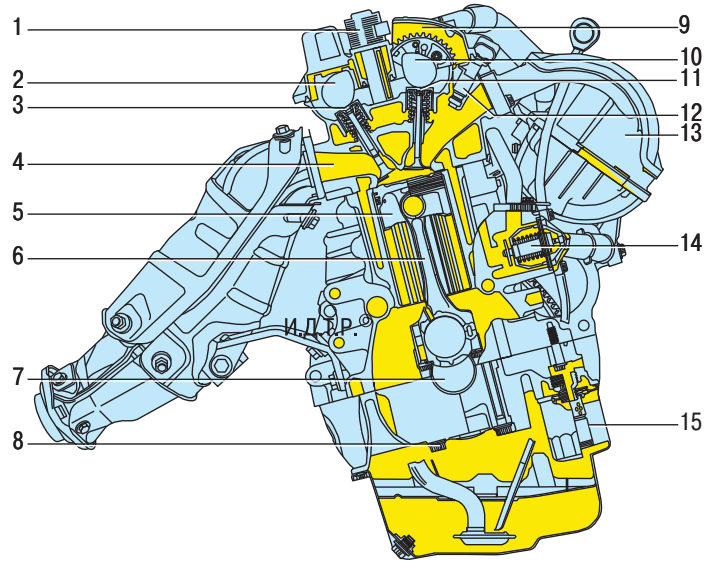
Двигатель 4ZZ-FE (поперечный разрез): 1 – катушка зажигания; 2, 10 – распределительные валы; 3, 11 – толкатели; 4 – выпускной коллектор; 5 – поршень; 6 – шатун; 7 – коленчатый вал; 8 – масляный насос; 9 – крышка головки блока цилиндров; 12 – форсунка; 13 – впускная труба; 14 – термостат; 15 – масляный фильтр
